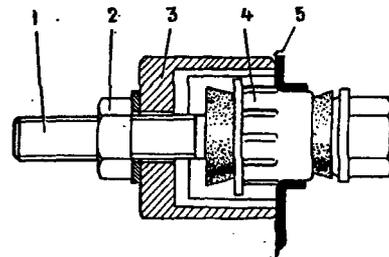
Схема выпрессовки шарнира верхнего рычага: 1 - болт; 2 - гайка; 3 - стакан приспособления А.47046; 4 - шарнир; 5 - верхний рычаг
